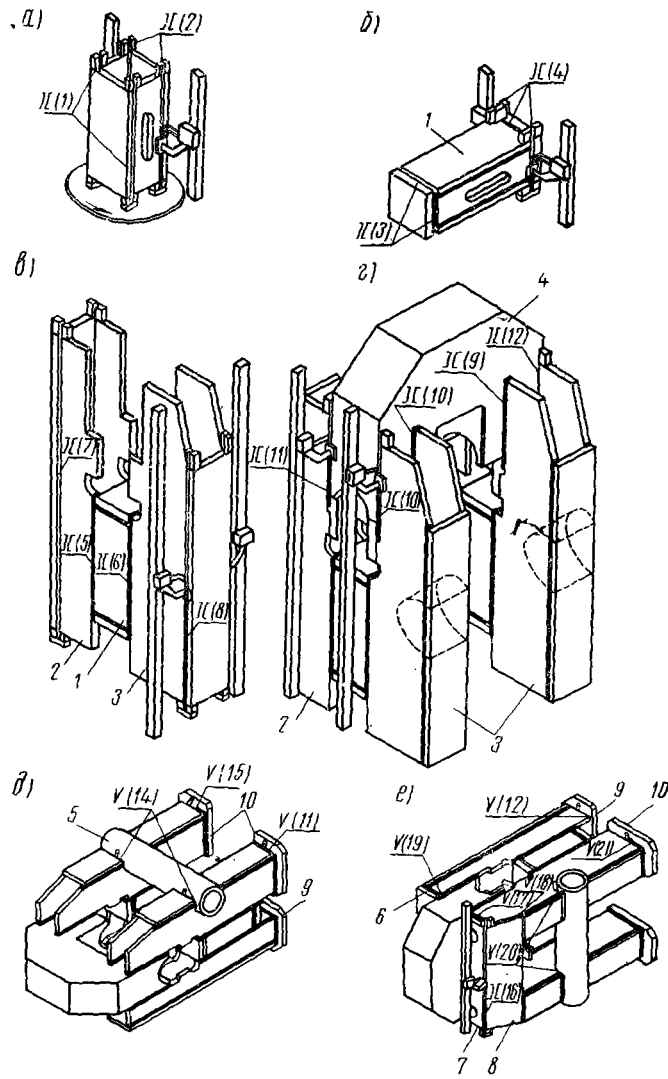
Последовательность сборочно-сварочных операций при изготовлении станины прессы усилием 4000 Т
